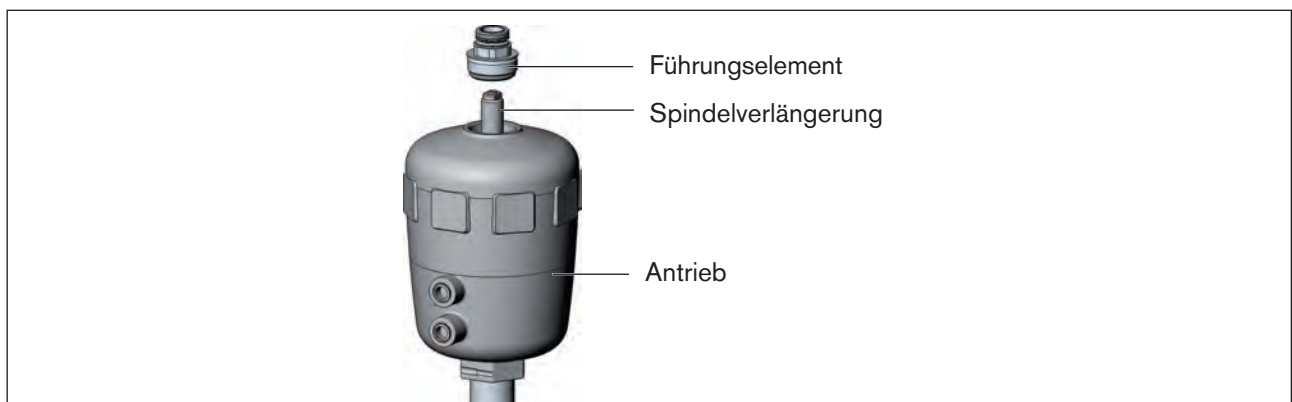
Montage der Schaltspindel (1), Reihe 26xx und 27xx
